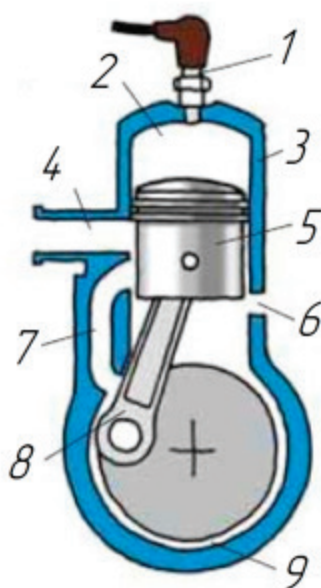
а. Конструкция двигателя и его расчетная схема (конструкция двухтактного двигателя с кривошипно-камерной продувкой): 1 — свеча зажигания, 2 — камера сгорания, 3 — цилиндр, 4 — выпускной канал, 5 — поршень, 6 — впускное окно в кривошипную камеру, 7 — продувочный канал, 8 — шатун, 9 — кривошипная камера
